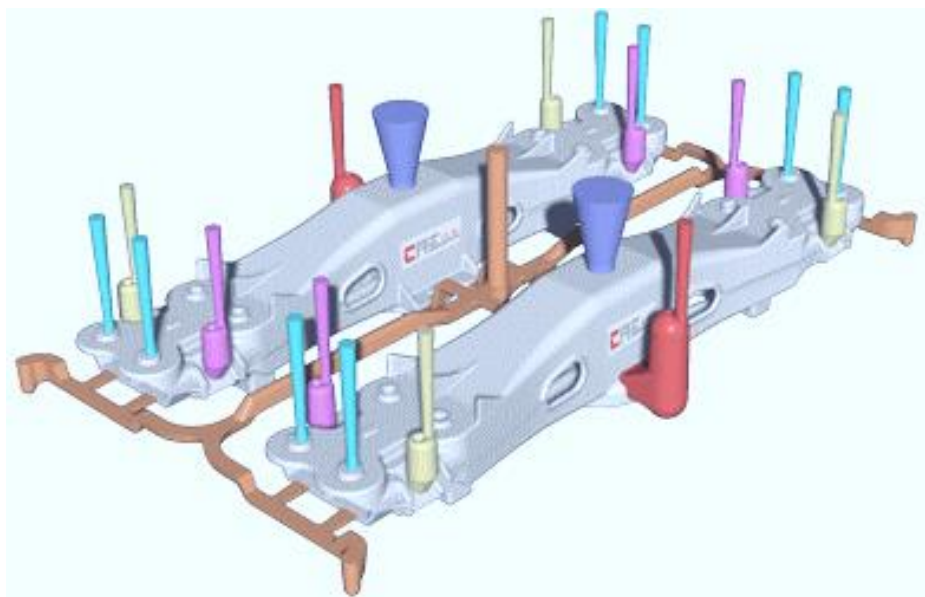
Литниковая система для отливки (балка под рессорная)
